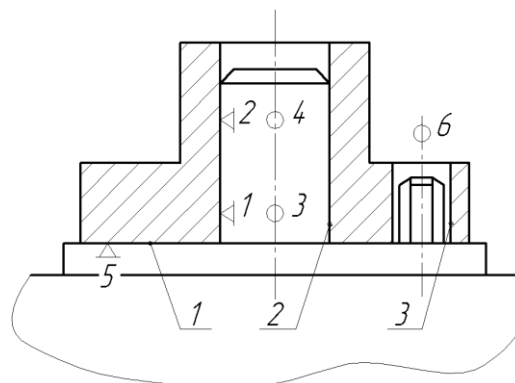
Базування заготовки корпуса фланцевого типу на площину,
